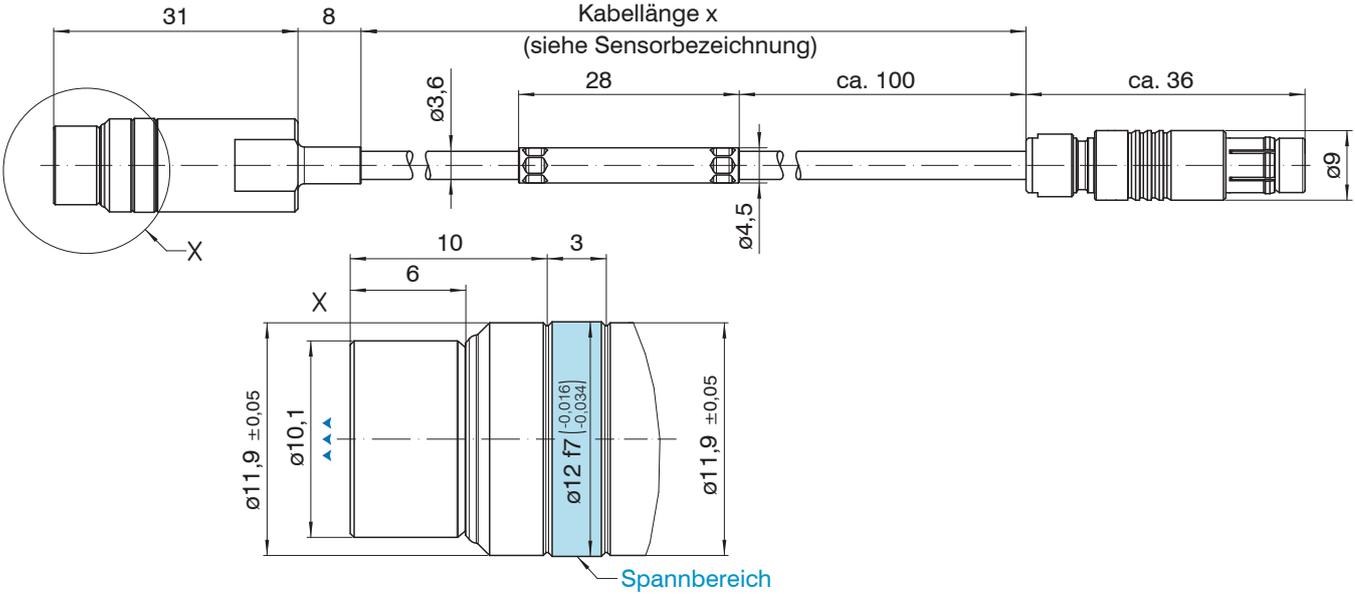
Maßzeichnung Sensoren ES-U3-T-CAx/mB0, Abmessung in mm
